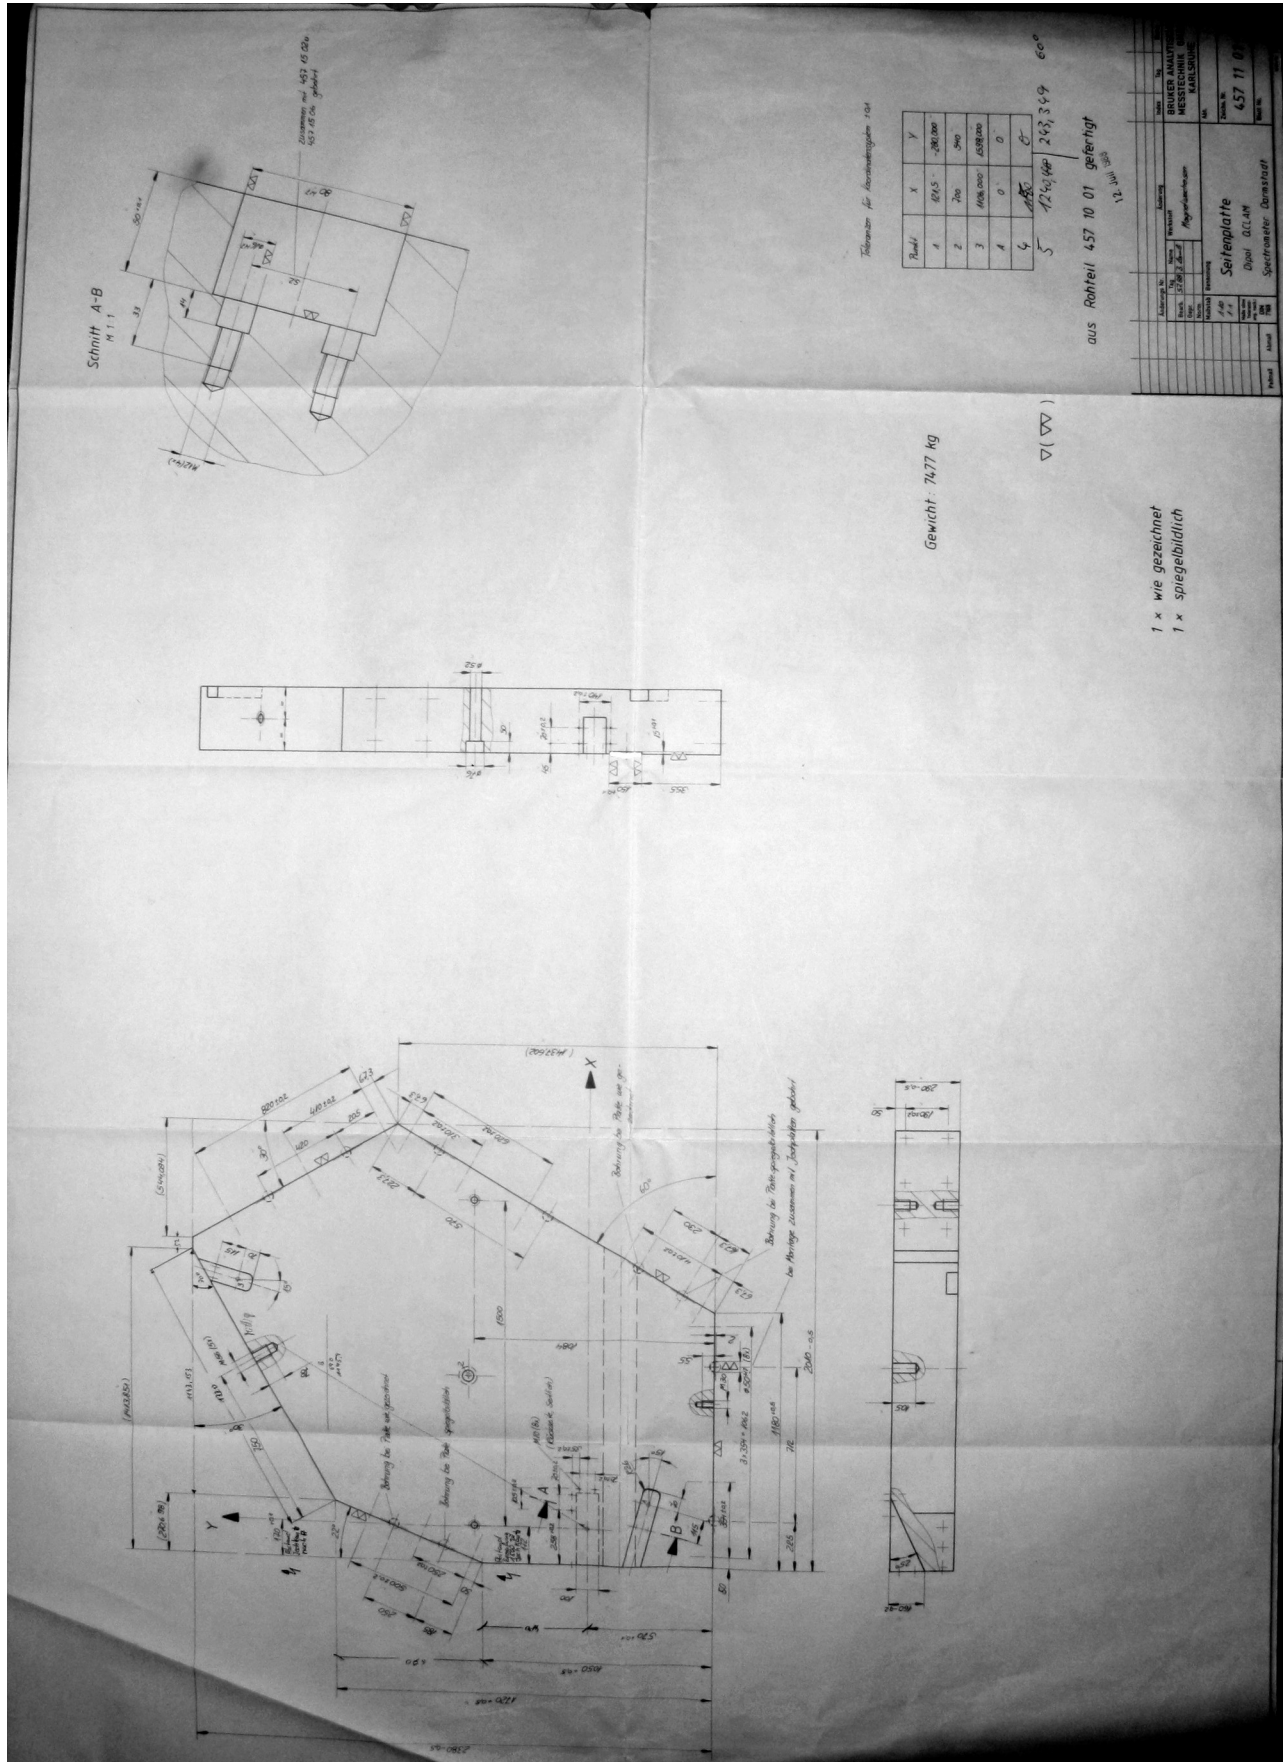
Technische Zeichnung der Seitenplatte des Jochs des QClams.
